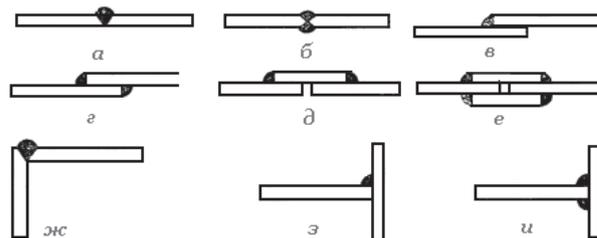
Основные типы сварочных соединений: а – стыковое с односторонним скосом кромок, б – стыковое с двусторонним скосом кромок, в – нахлесточное с одним швом, г – нахлесточное с двумя швами, д – стыковое с накладкой, е – стыковое с двумя накладками, ж – угловое, з – тавровое с одним швом, и – тавровое с двумя швами
